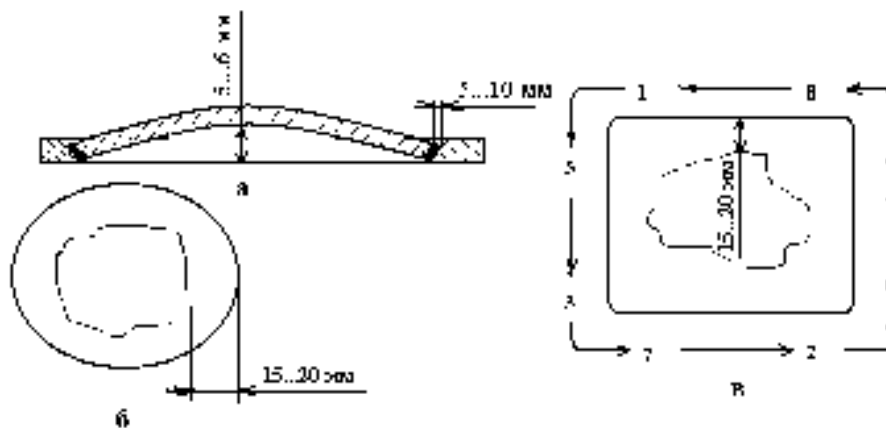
Заделка пробоины в чугунном корпусе стальной заплатой: *а* - схема установки заплаты; *б* и *в* - круглый и прямоугольный вырезы под заплату: (1...8-порядок наложения сварных швов по участкам)
